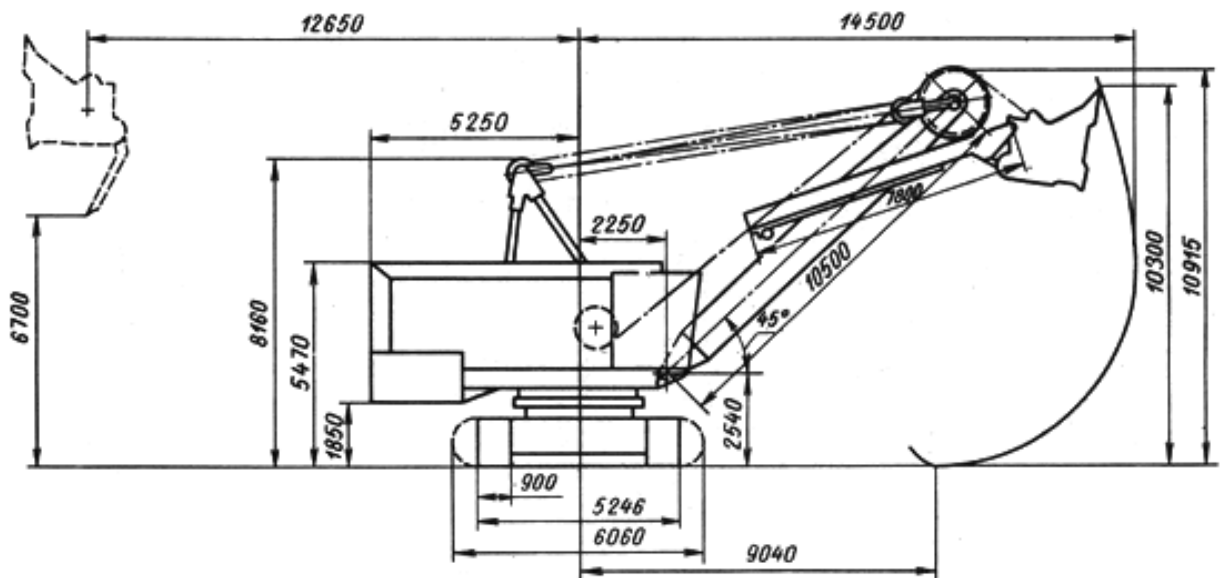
Зовнішній вигляд з габаритними розмірами екскаватору ЕКГ-5А
